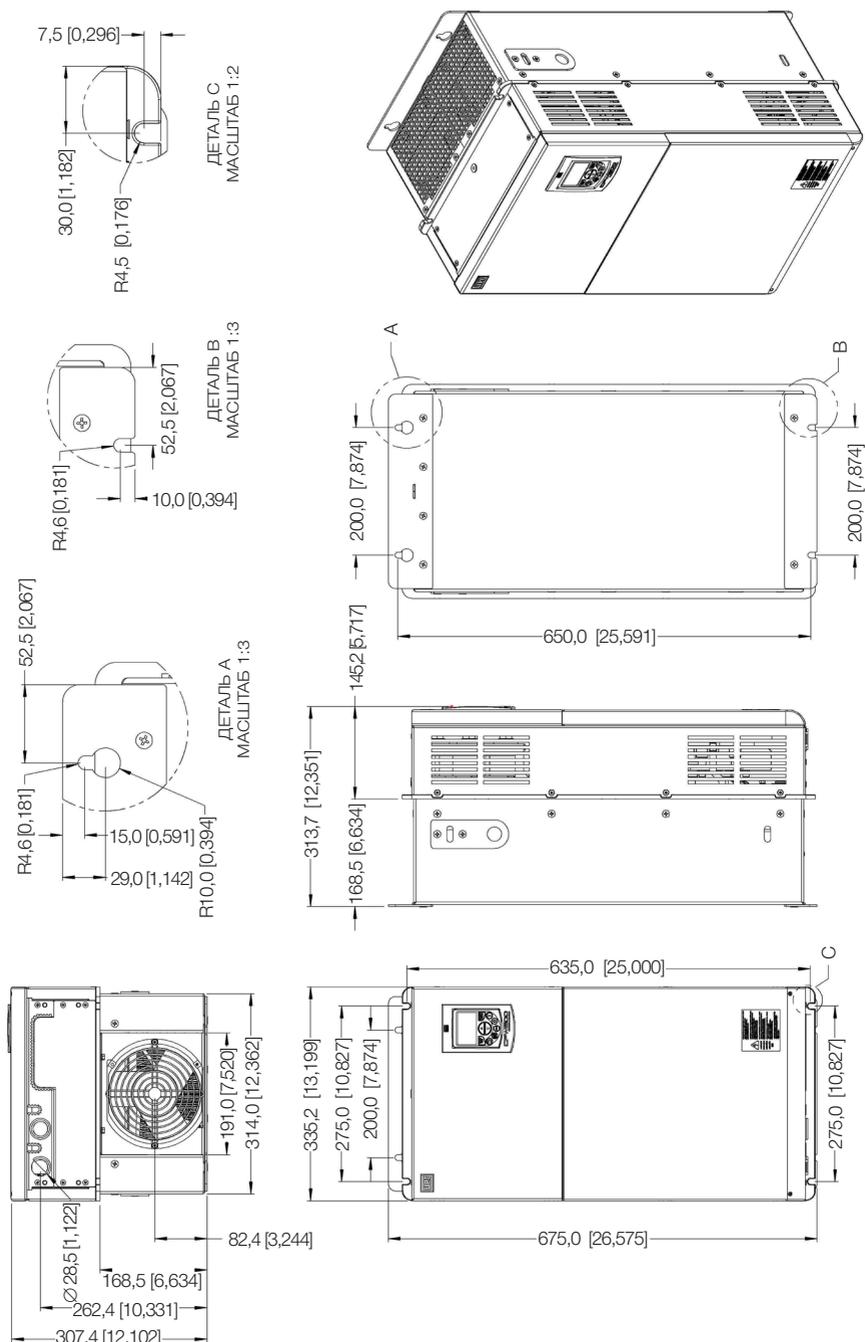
Размеры преобразователя в мм [дюйма] - типоразмер G
